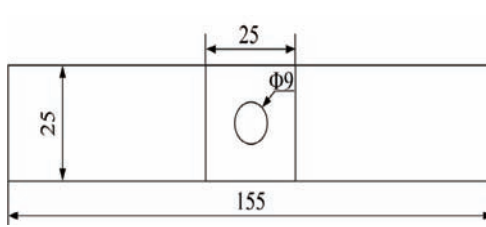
回填式搅拌摩擦点焊拉伸试样尺寸
